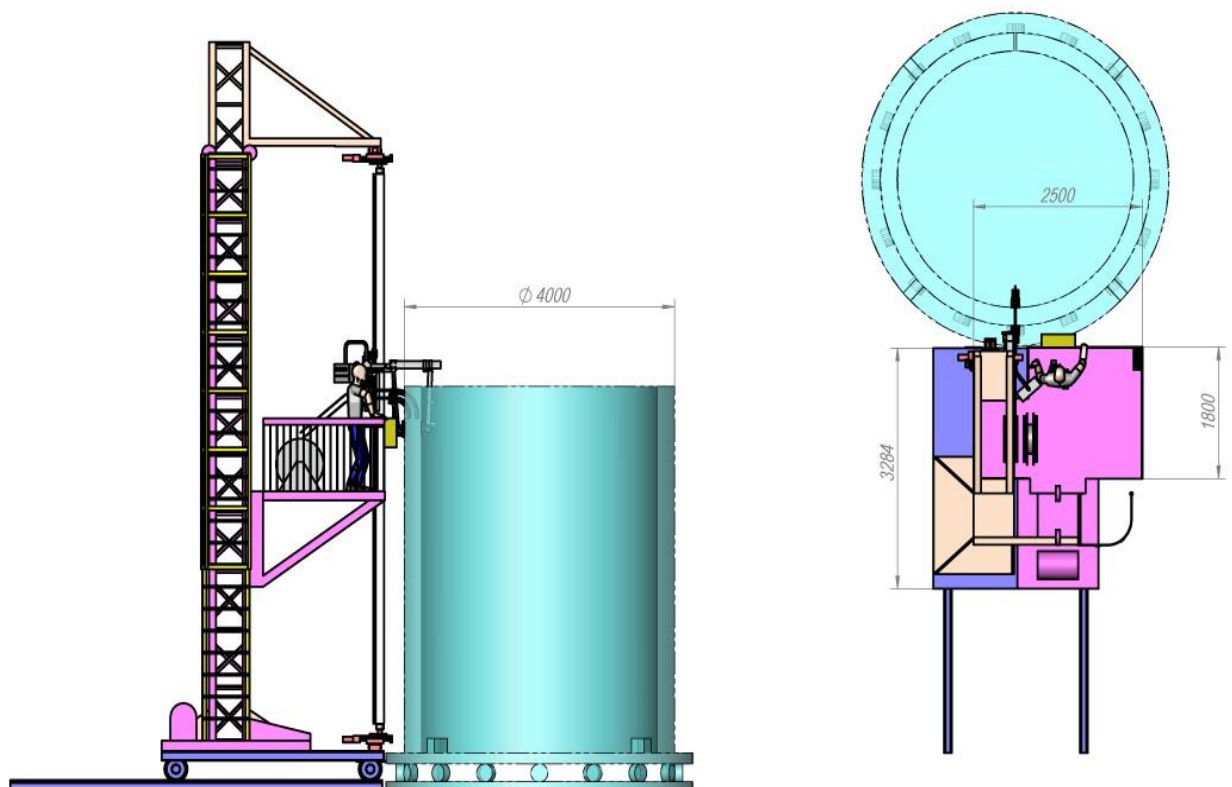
«Сварка обечаек установкой на платформе»[21]
